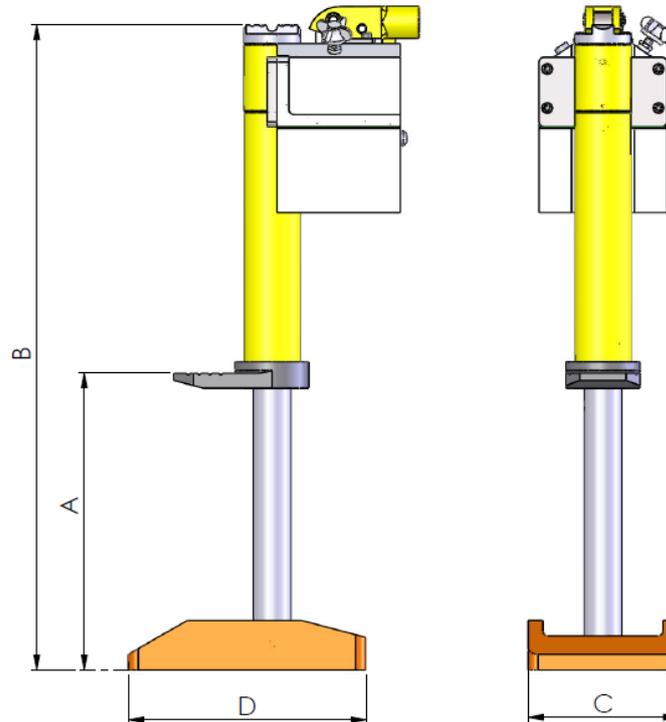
Dimensões do Macaco Hidráulico TMU1010 Aberto
